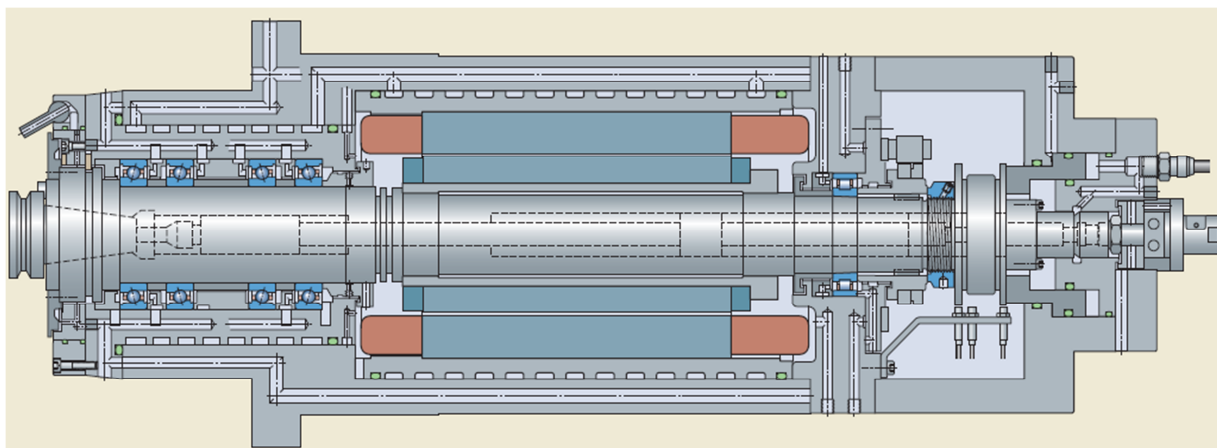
Схема мотор-шпинделя горизонтального обрабатывающего центра
